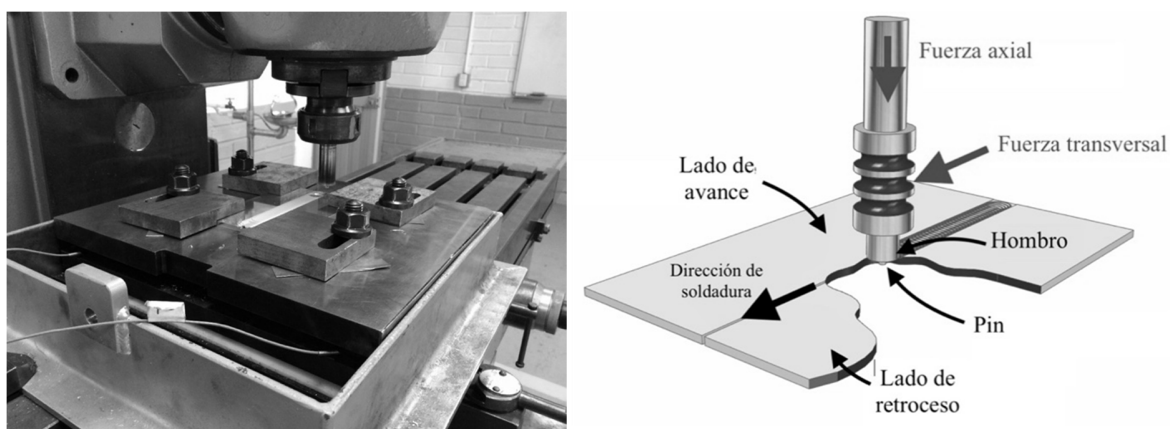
Montaje adaptado para la obtención de juntas soldadas por FSW con medición de fuerza vertical y esquemático de proceso.
